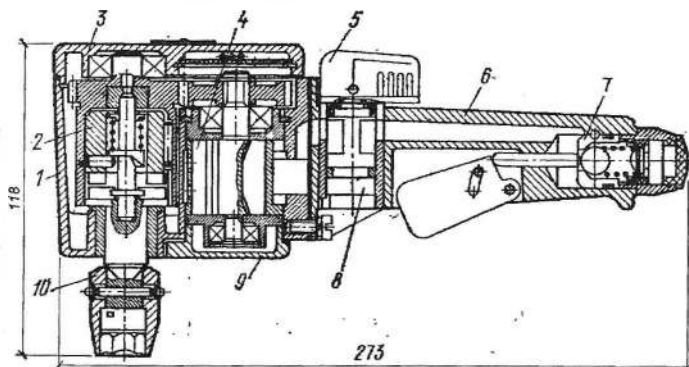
Пневматический угловой гайковерт ИП-3207А:
